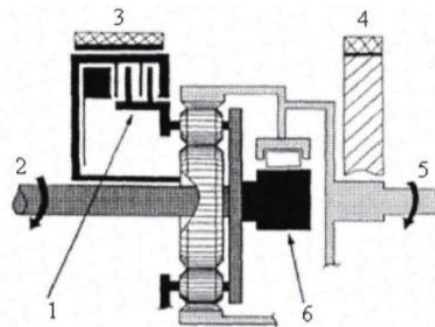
Підвищувальний планетарний ряд: 1 - блокувальна муфта; 2 - вал турбінного колеса; 3 - гальмо МЦК; 4 - картер; 5 - вхідний вал основної частини коробки передач; 6 - муфта вільного ходу [15] - [23].
